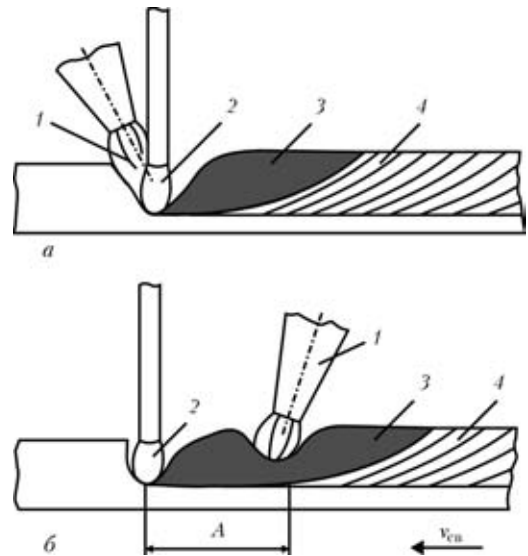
Схема гибридной сварки дуга + газовое пламя: а — газовое пламя расположено перед дугой; б — за дугой; 1 — газовое пламя; 2 — электрическая дуга; 3 — сварочная ванна; 4 — шов
